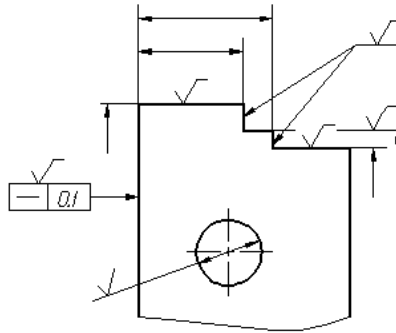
Примеры расположения обозначения шероховатости
